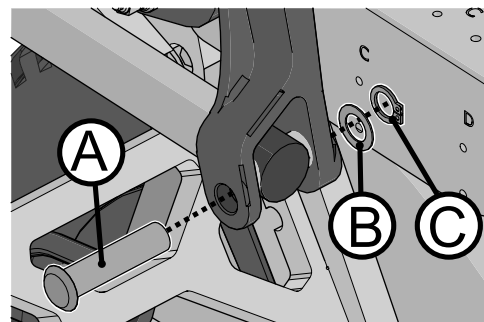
Die neue hintere Befestigung der Stellvorrichtung.
